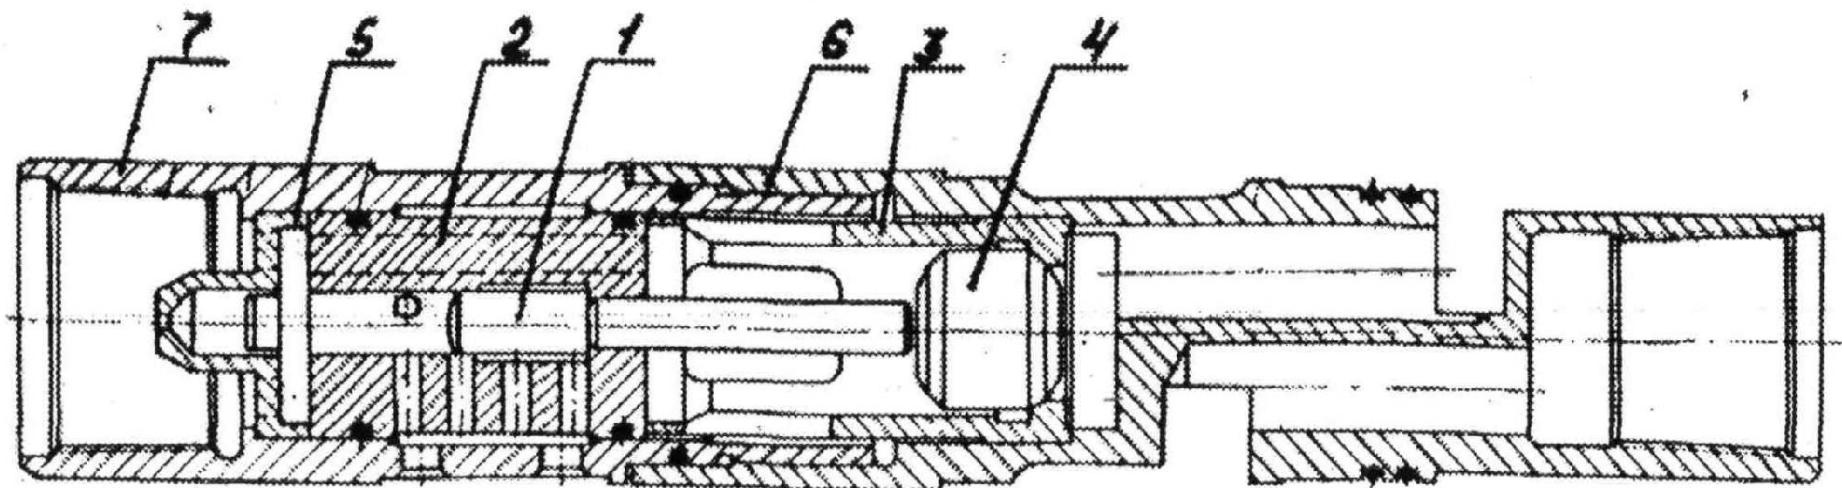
Предохранительный клапан поршенько-золотниковый
